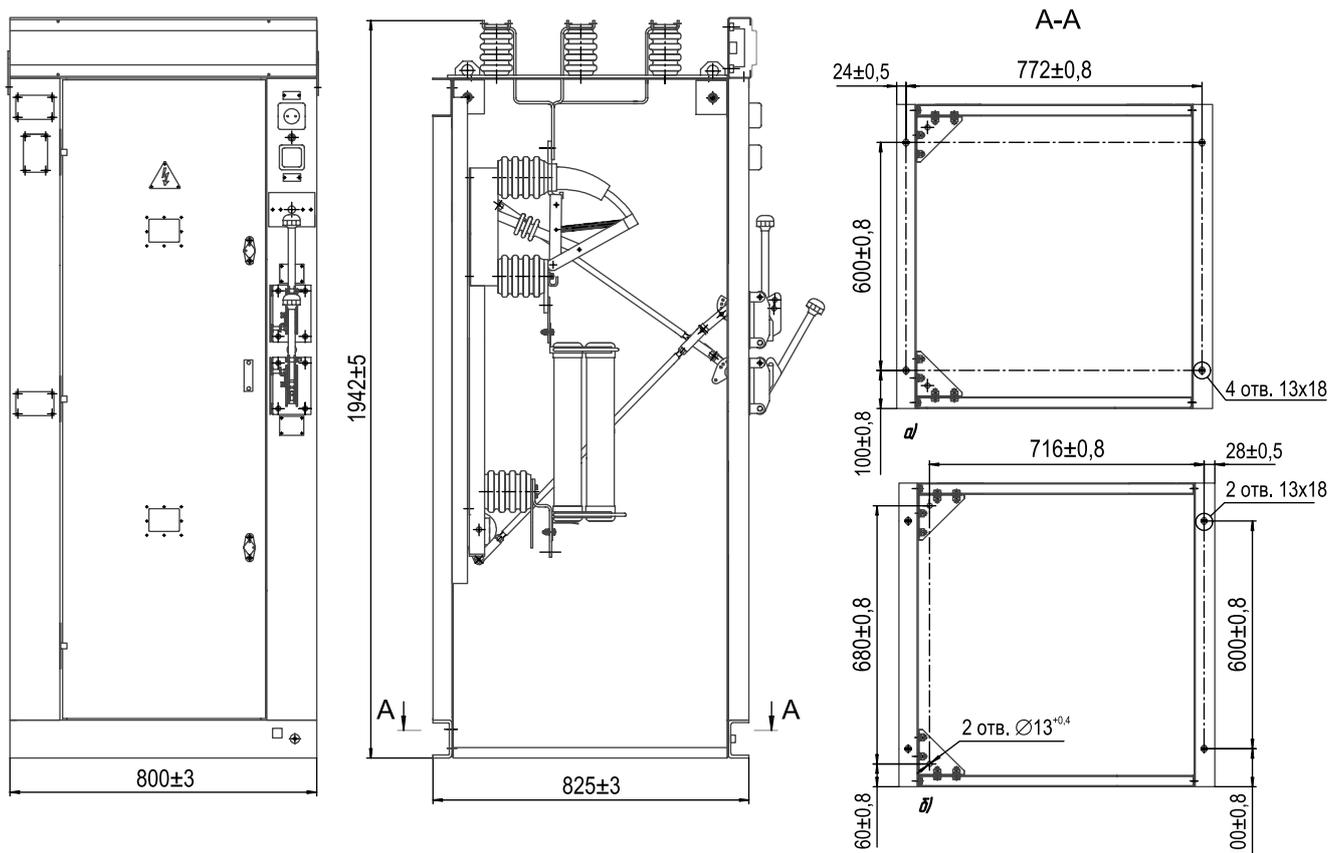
Габаритные, установочные, присоединительные размеры КСО-306 с автогазовым выключателем нагрузки ВНА-10/630:
